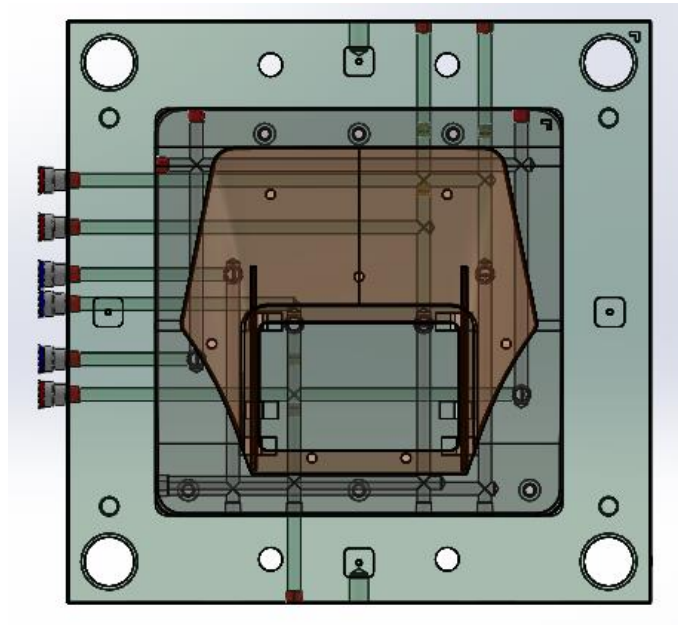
Sistema de refrigeración parte móvil - Vista planta
